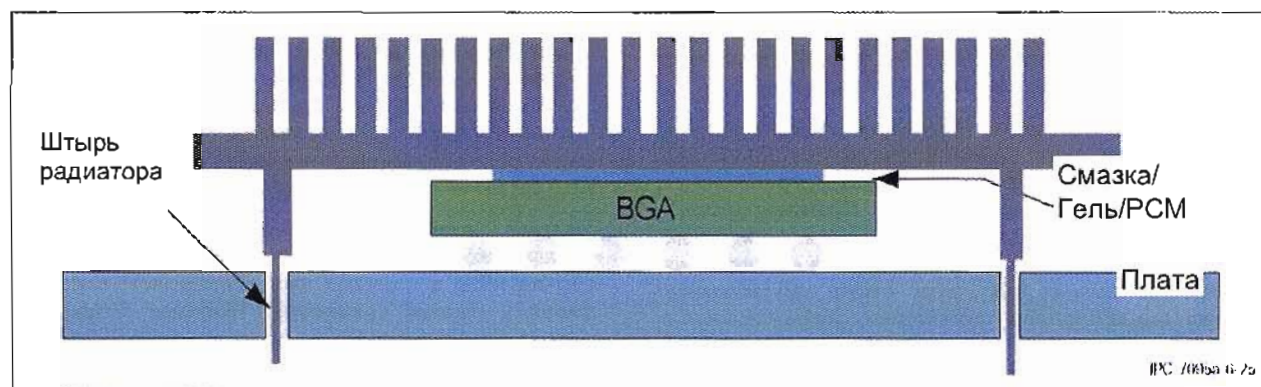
Радиатор, установленный на корпус BGA при помощи штырьков, впаянных в сквозные отверстия печатной платы
